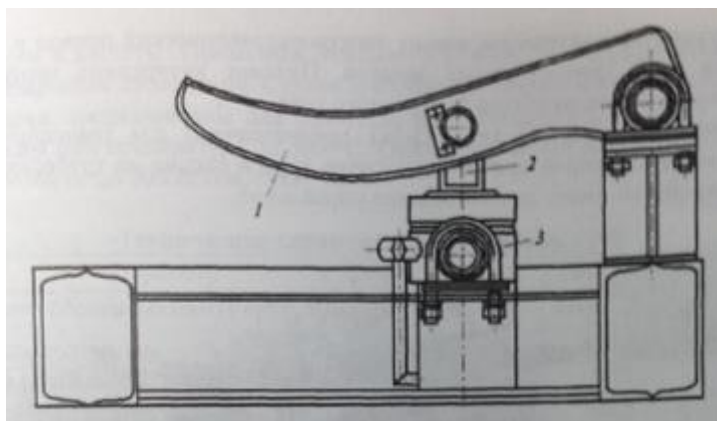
Перегрузатель на трубосварочной линии: 1 - рычаг; 2 - шток; 3 - цилиндр.
